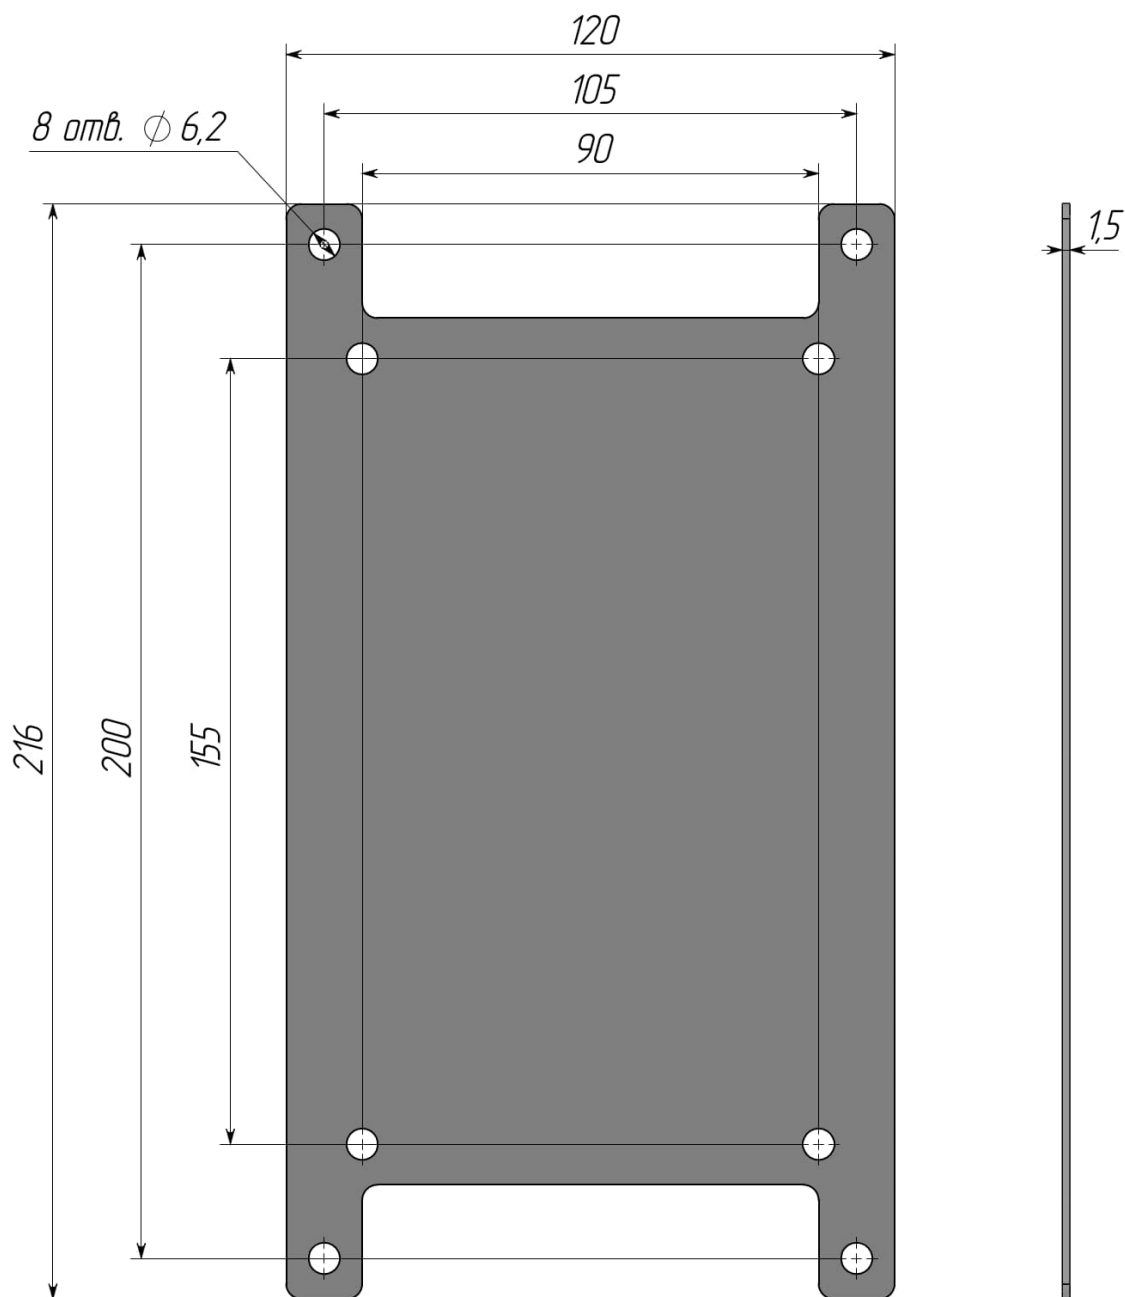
Габаритные и установочные размеры планки 1 для установки вторичного преобразователя конструктивного исполнения корпуса – настенный алюминиевый.
